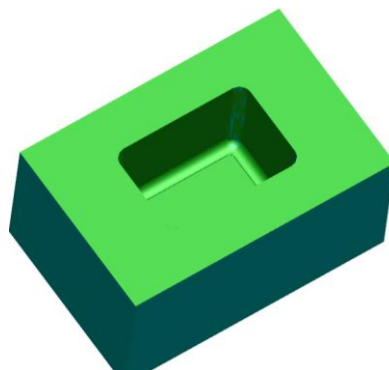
Аналіз прогнозованої точності чистового фрезерування стінок призматичного заглиблення
